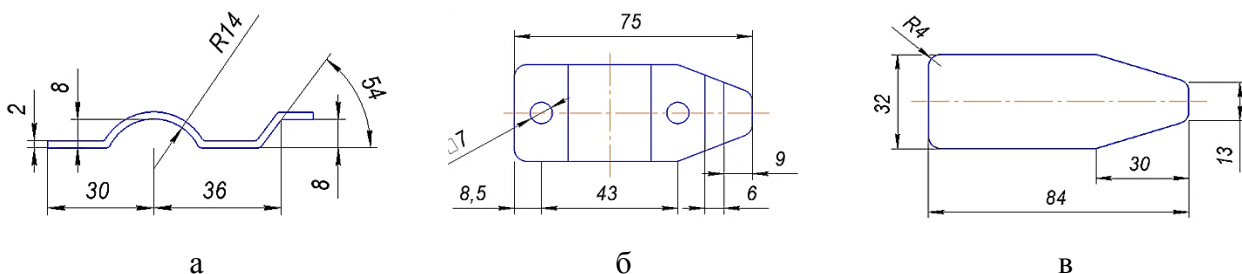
Ползун: а – вид сбоку; б – вид сверху; в – развертка
